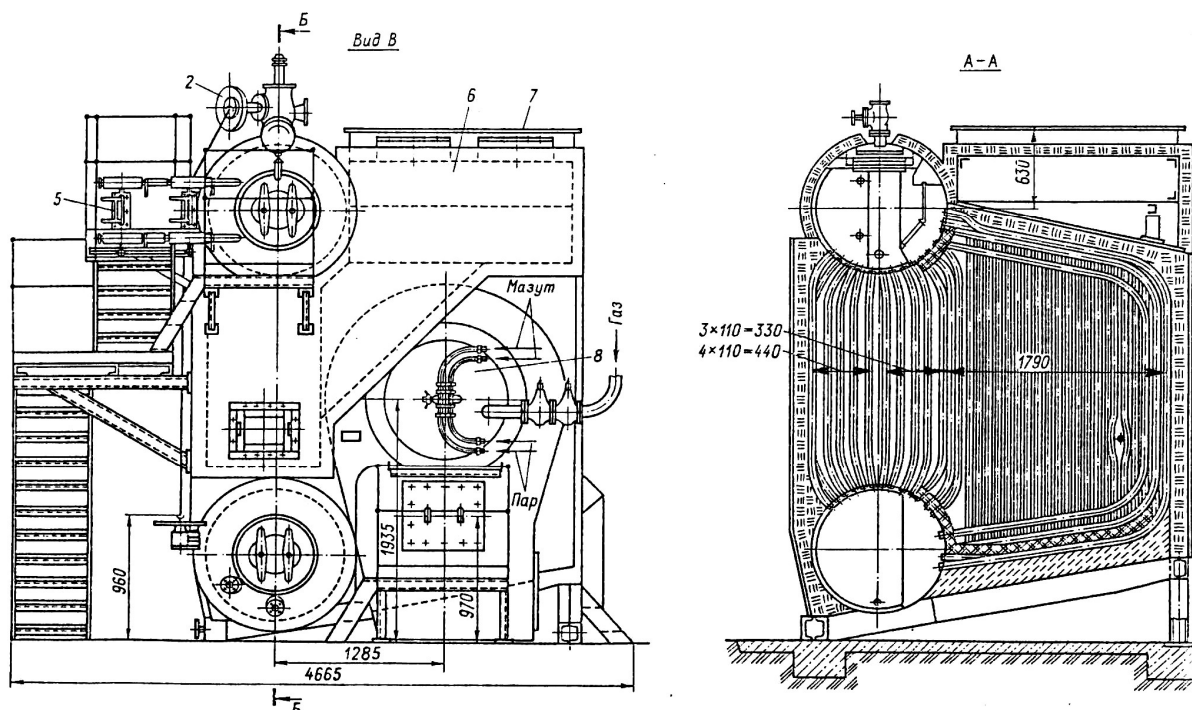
Конструкція та поперечний переріз котла марки ДЕ-10-14
